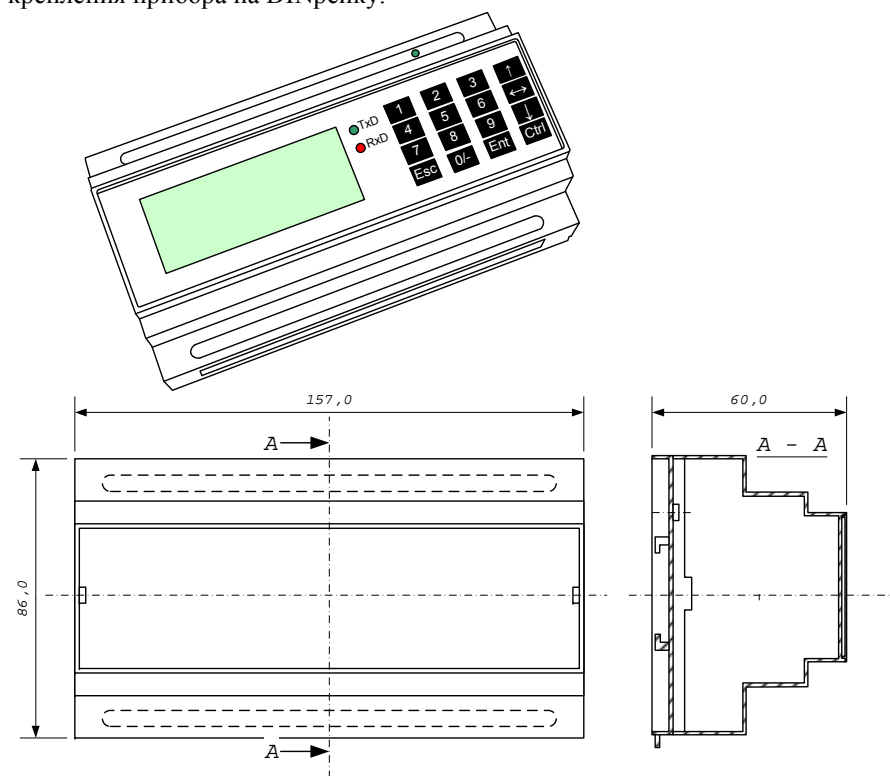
Внешний вид контроллера «БиКуб-РТ04»
